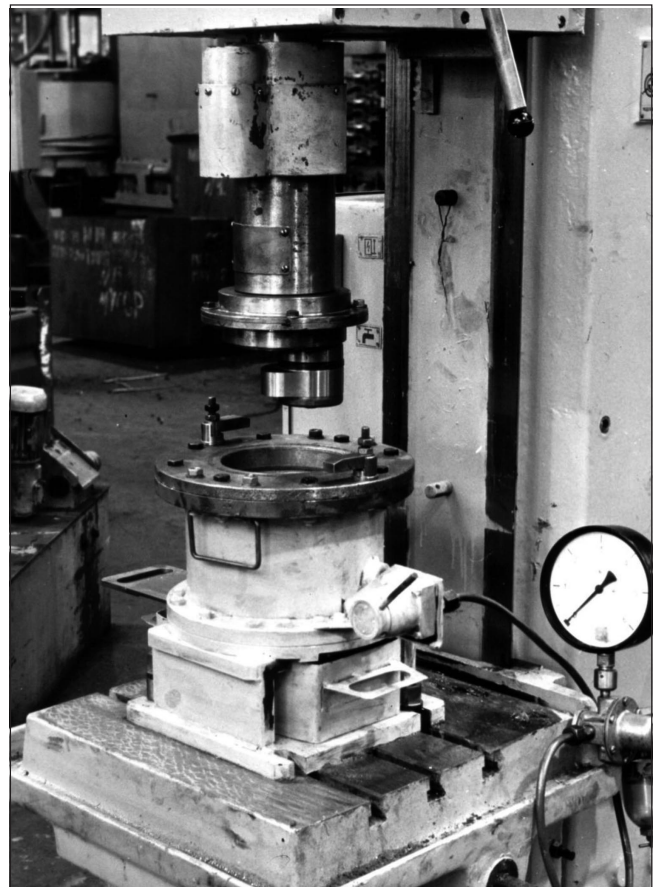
Общий вид варианта промышленной установки для полирования деталей предлагаемым камерным способом в уплотненной обрабатывающей среде
